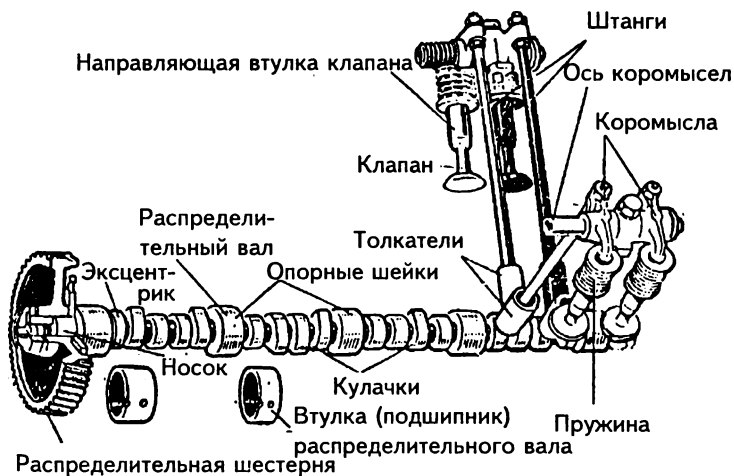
Газораспределительный механизм V-образного двигателя с верхним расположением клапанов
